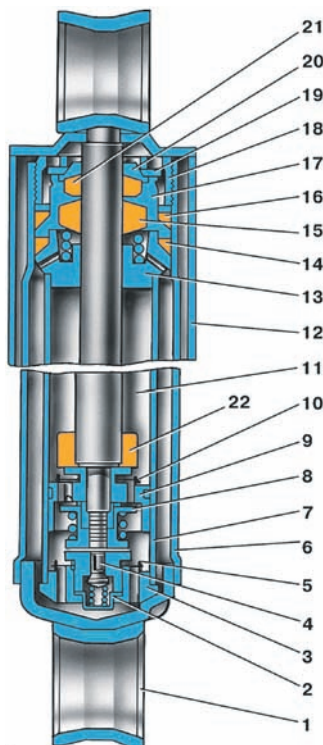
Амортиза тор: 1 - вушко; 2 - обмежувач клапана стиснення; 3 - корпус с клапана стиснення; 4 - клапан стиснення; 5 - впускний клапан; 6 - резервуар; 7 - циліндр; 8 - клапан віддачі; 9 - поршень; 10 - перепускний клапан; 11 - шток; 12 - кожу; 13 - напрямна втулка штока; 14 - нижнє кільце ущільнювача; 15 - сальник; 16 - верхнє кільце ущільнювача; 17 - обойма сальників; 18 - гайка резервуара; 19 - шайба; 20 - захисне кільце; 21 - сальник штока; 22 - б'єр відбою (для пружинної підвіски)
